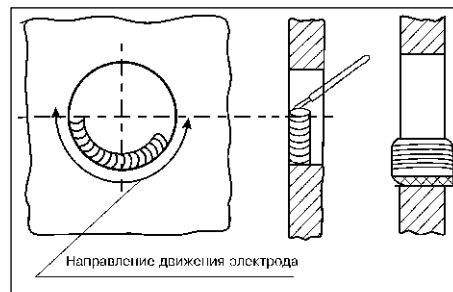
Схема обварки отверстия с целью уменьшения размеров пробки
